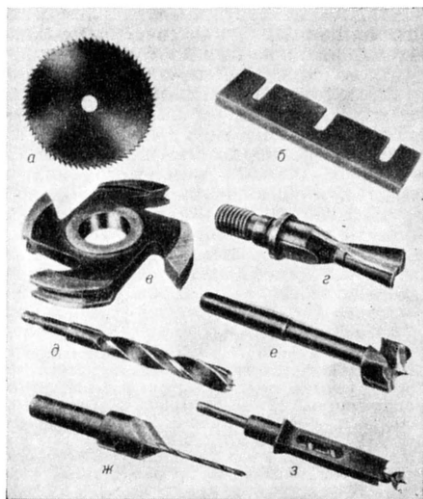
Девеорежущий станочный инструмент: а — дисковая пила; б — строгальный нож; в — фреза фасонная; г — фреза концевая; д, е — сверла; ж — зенкер; з — долото.
